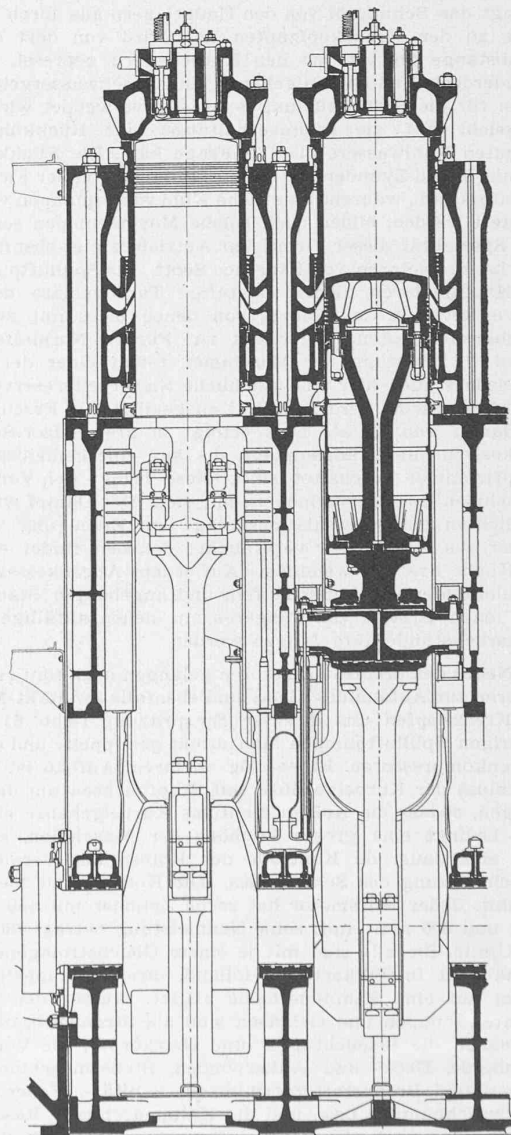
Längsschnitt durch zwei Zylinder einer Hauptmaschine
